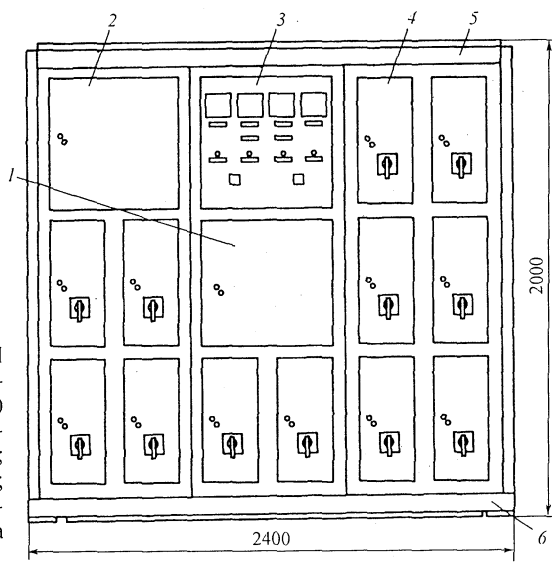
Вариант конструкции РУНН с выдвигаемыми выключателями (габаритные размеры, мм: 2400 × 2000 × 825) (исполнение с АВР — неявный ввод резерва): 1 — шкаф выключателя ввода; 2 — шкаф секционного выключателя; 3 — шкаф релейный; 4 — шкаф линейного выключателя; 5 — рама; 6 — рама основания
